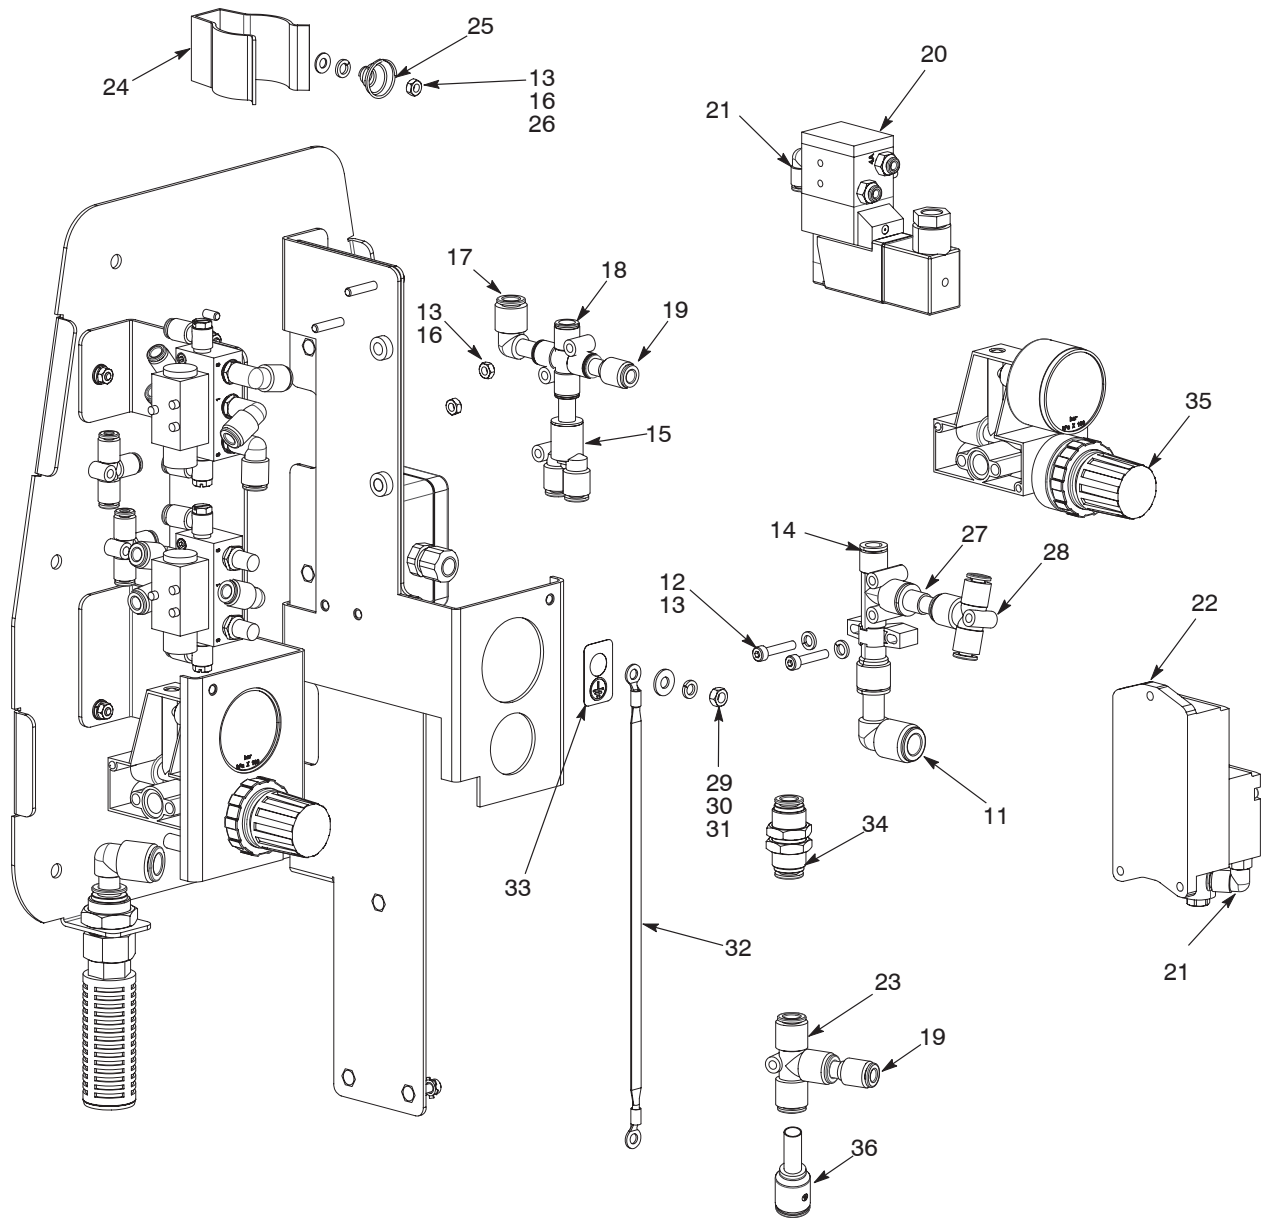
Comandi della pompa - lato destro (qui nella versione con generatore)
